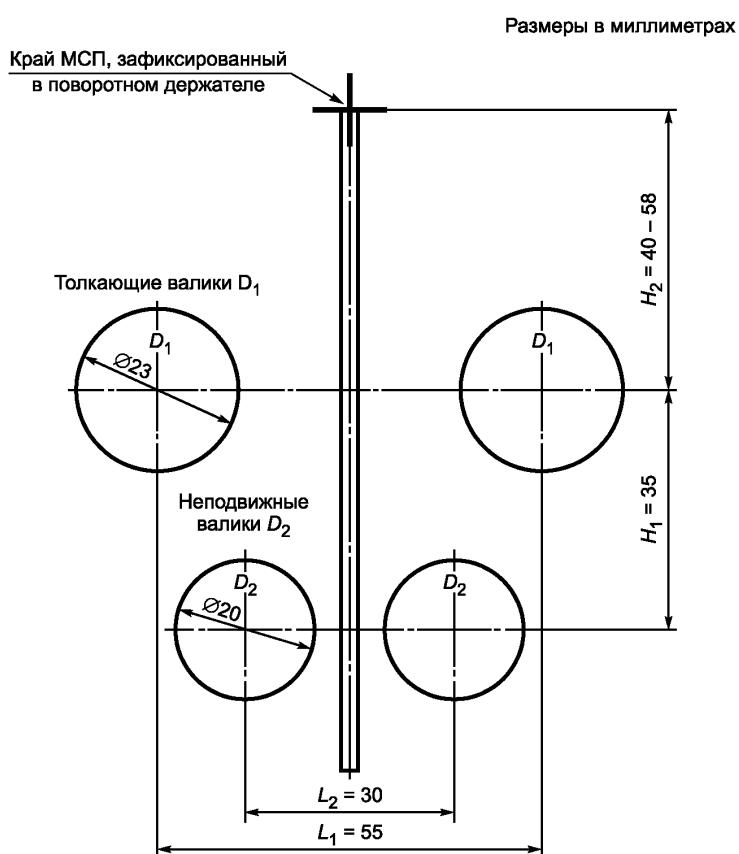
Схема испытательного стенда для проведения испытаний на изгиб
